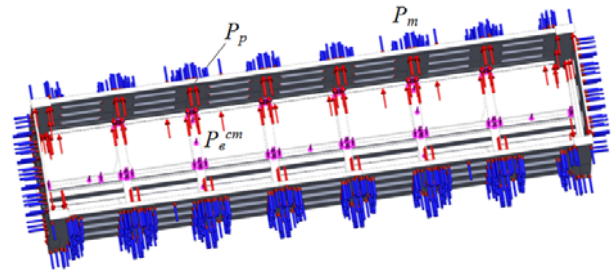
Розрахункова схема несучої конструкції напіввагона
